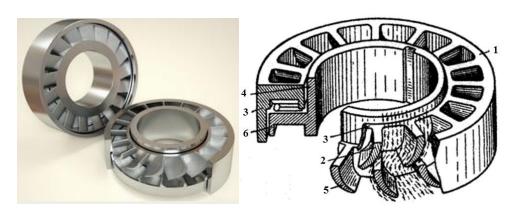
Общий вид статора и ротора турбобура и принцип действия турбины: 1 — наружное кольцо статора; 2 — лопатки статора; 3 — внутренний обод статора; 4 — внутренне кольцо ротора; 5 — лопатки ротора; 6 — наружный обод ротора.
